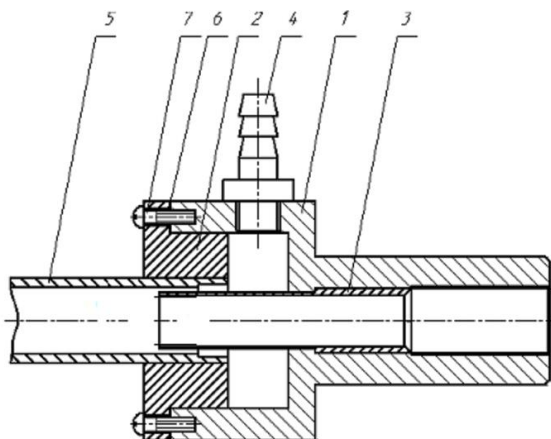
Устройство для создания пристенного кольцевого слоя: 1 – корпус; 2 – втулка; 3 - гильза; 4 – штуцер; 5 – труба; 6 – прокладка; 7 – винт
